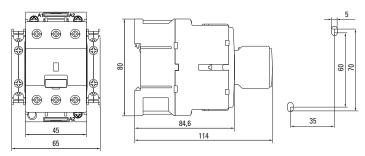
Габаритные и установочные размеры контакторов КМЭ 32А, КМЭ 38А
